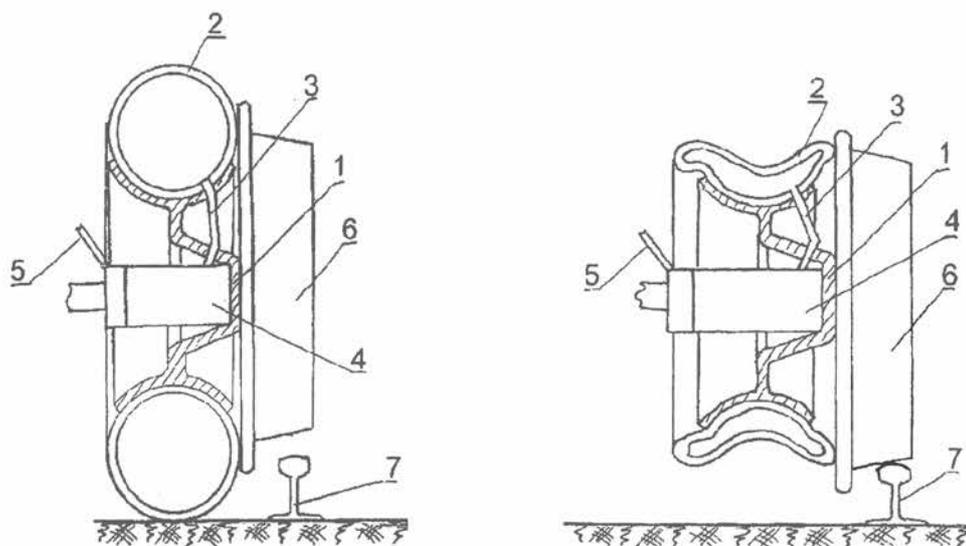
Приводной комбинированный ход, совмещенный с ведущими колесами транспортного средства:
